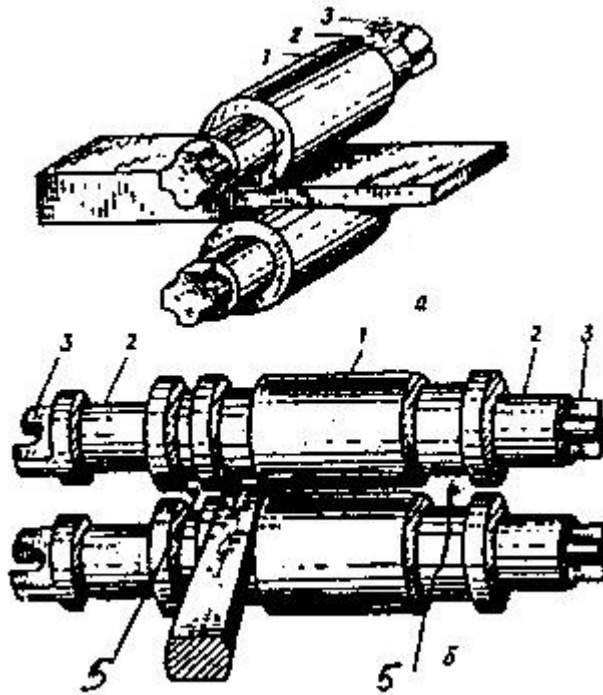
Прокатка на гладкій (а) і каліброваній бочці (б); 1 – бочки валків; 2 – шийки валків; 3 – трефи; 4 – прокатувана штаба; 5 – калібри
